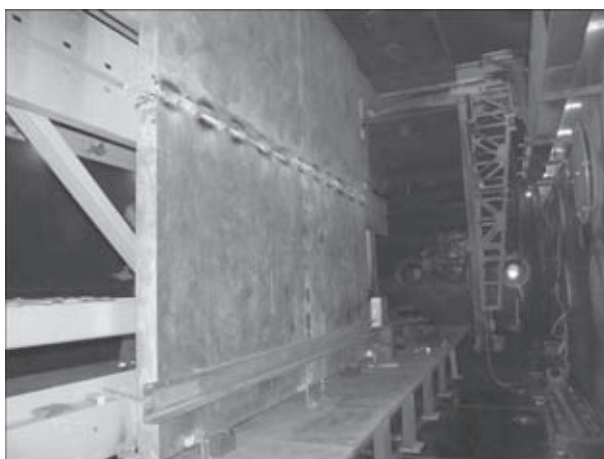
Общий вид платформы из сплава МА2 перед выполнением сварки последнего шва длиной 3000 мм
